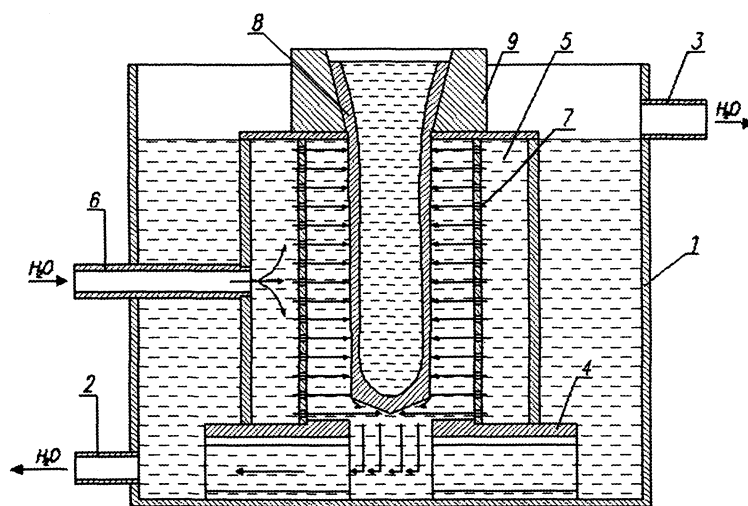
Устройство для охлаждения отливок: 1 – бак; 2 – отводящий патрубок; 3 – сливной патрубок; 4 – опорный стол; 5 – кольцевой коллектор; 6 – подводящий патрубок; 7 – отверстия; 8 – отливка; 9 – захват
